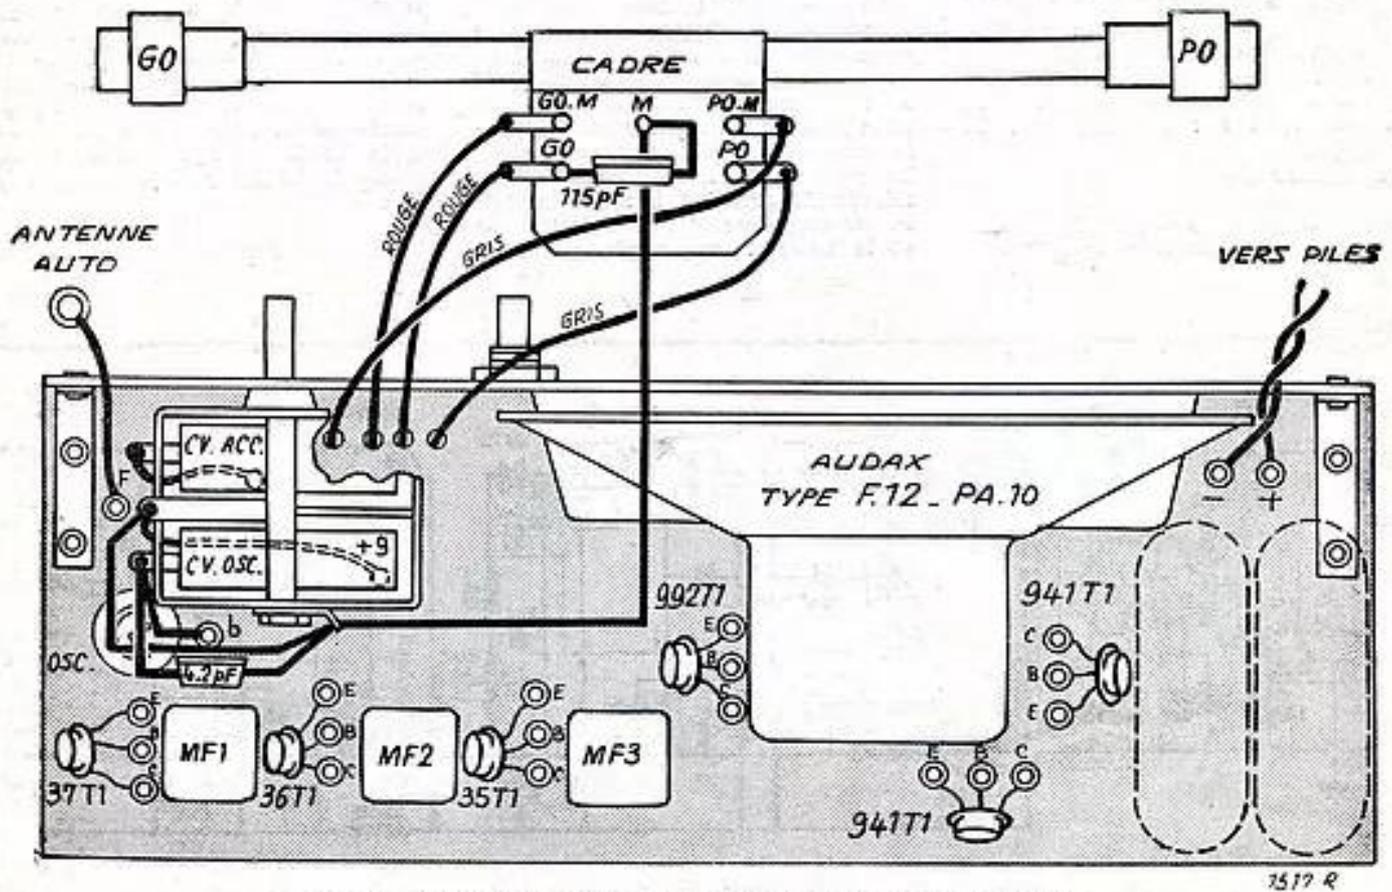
Disposition des pièces sur le dessus du châssis et leur câblage.
